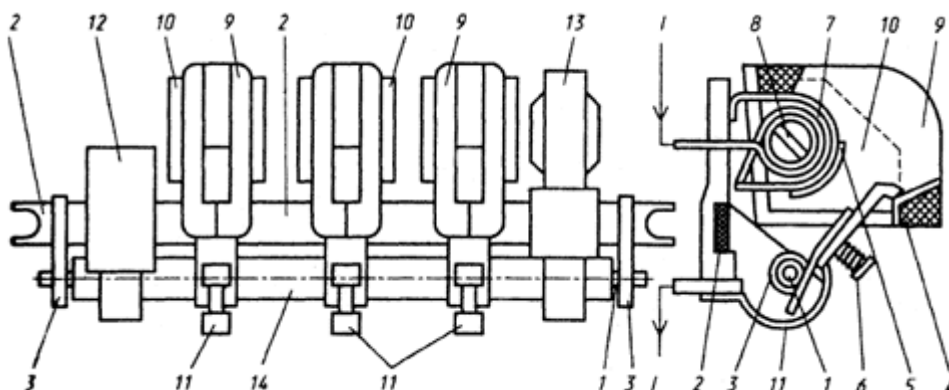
Конструктивная схема контактора КТ6000:1 - вал; 2 - металлическая изолированная рейка; 3 - подшипники; 4 и 5 - подвижный и неподвижный контакты; 6 - контактная пружина; 7 - катушка магнитного дутья (МД); 8 - сердечник системы МД; 9 - дугогасительная камера; 10 - полосы системы МД; 11 - гибкая медная связь; 12 – узел вспомогательных контактов; 13 - электромагнит; 14 - изоляционный слой на металлическом валу; I - коммутируемый ток
